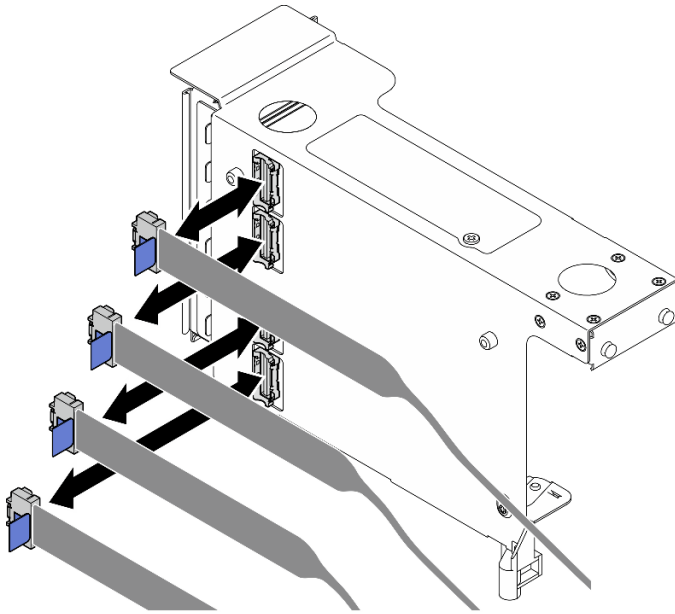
Desconectando cabos PCIe do exterior da placa riser
